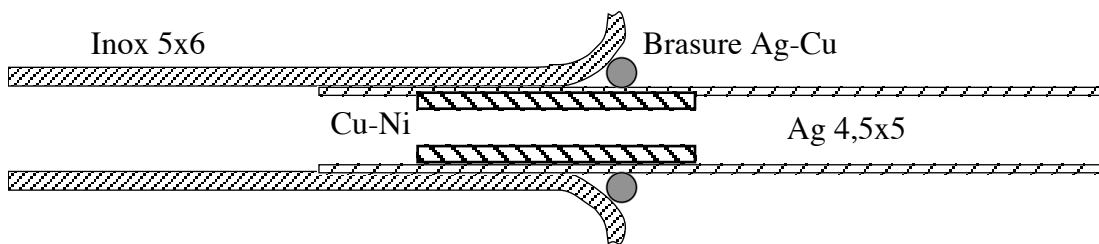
Dessin de la soudure expliquée dans le texte ci-dessus.
